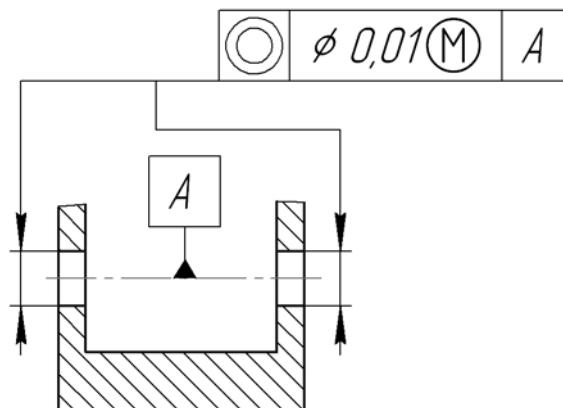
Простановка допуска расположения поверхностей
